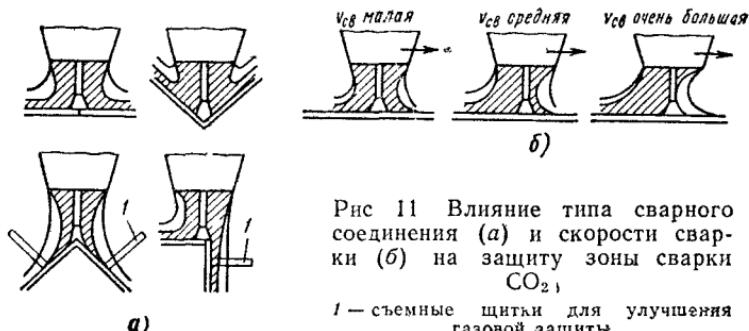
Влияние типа сварного соединения (а) и скорости сварки (б) на защиту зоны сварки CO_2 ,
